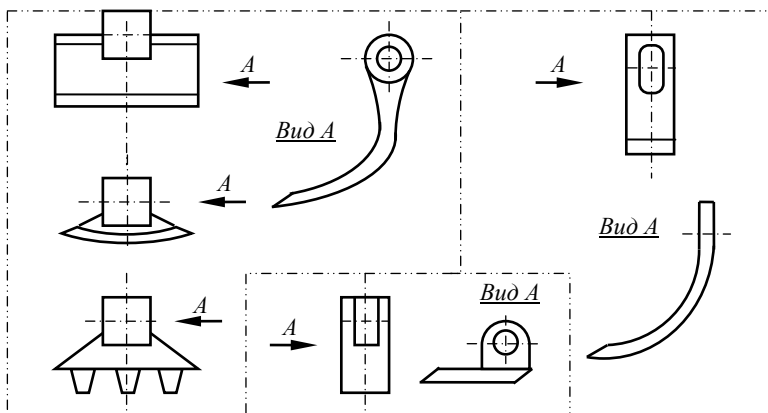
Ножи косилки-измельчителя с шарнирно закрепленными Г-образными ножами
